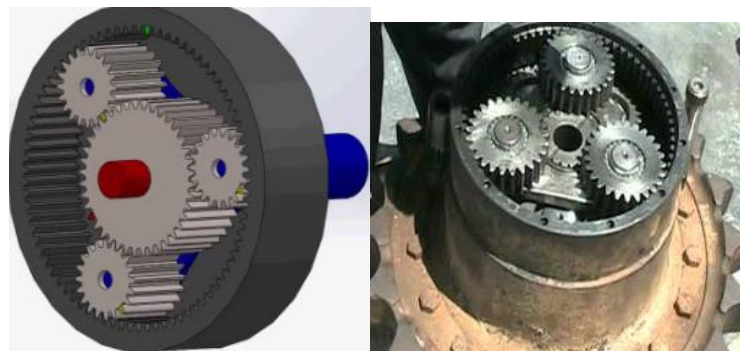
Engranajes planetarios y reductor de engranajes planetarios.
